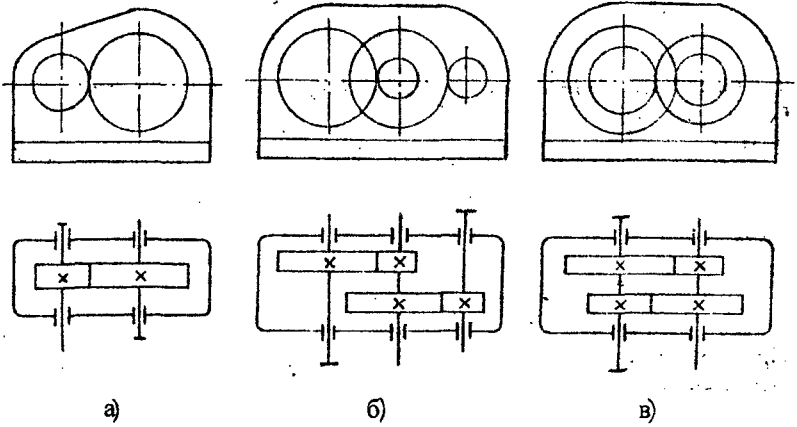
Кинематические схемы редукторов (по типу передачи)
